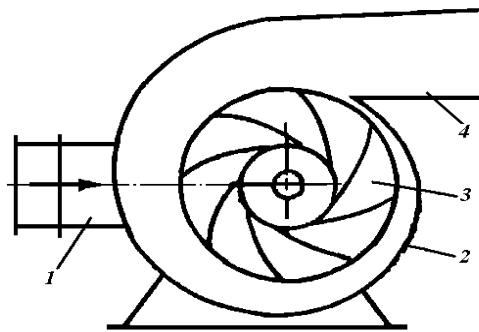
Схема відцентрового насоса: 1– вхідний патрубок; 2– корпус; 3– робоче колесо; 4– патрубок виходу рідини.
